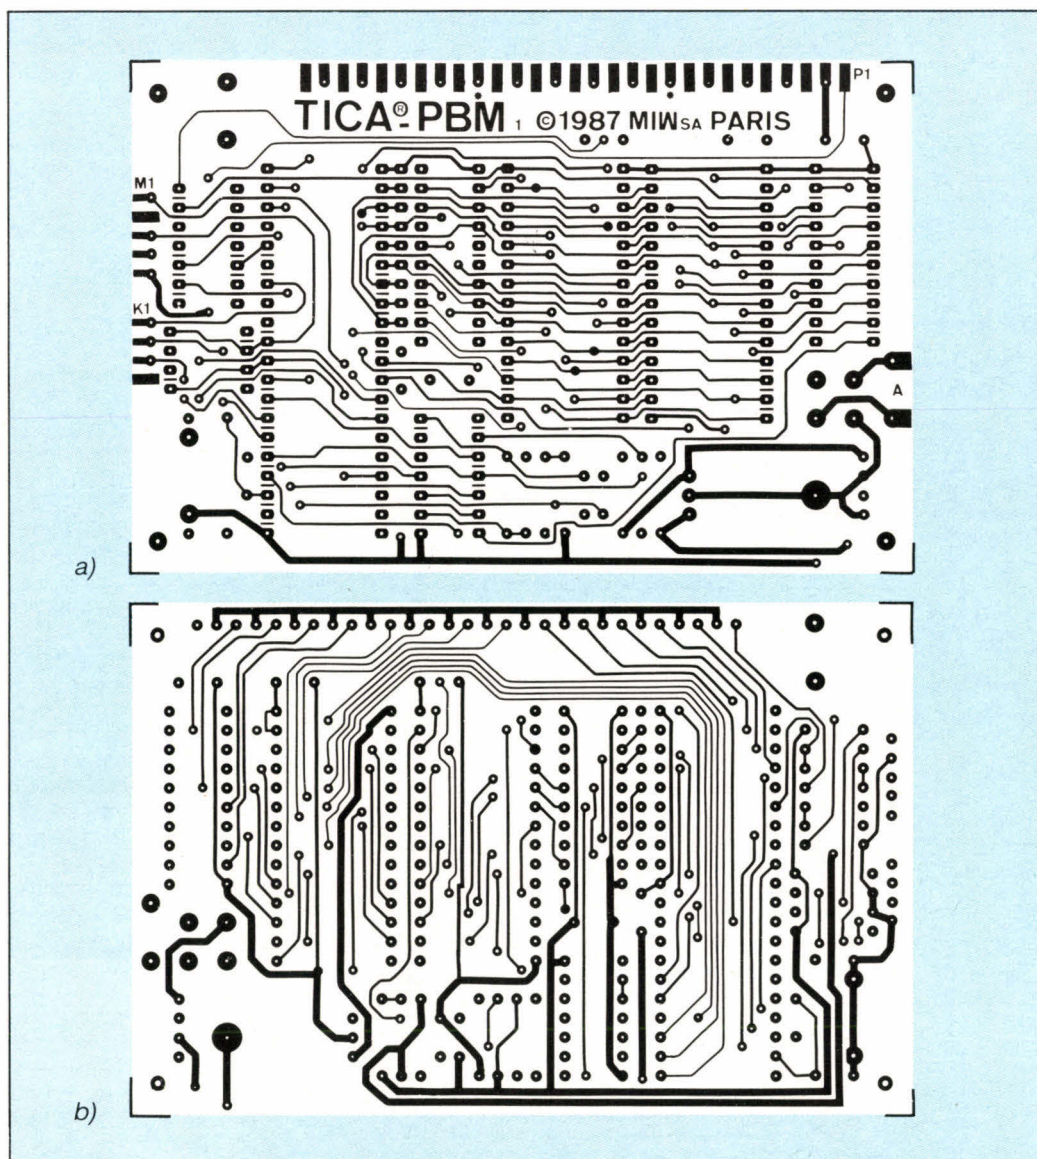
Circuit imprimé : a) côté composants ; b) côté soudures.
